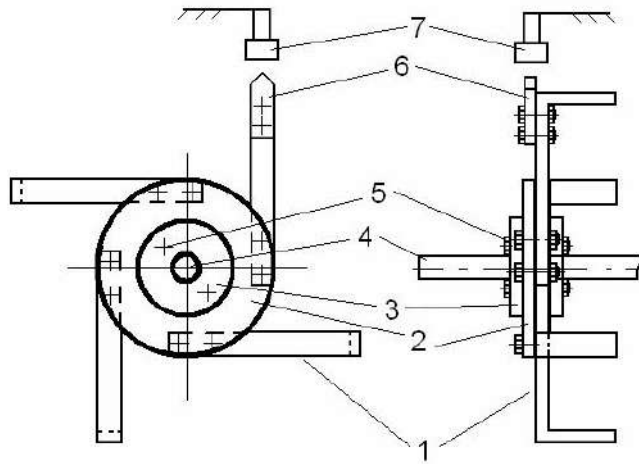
Схема устройства секции почвообрабатывающей фрезы.
